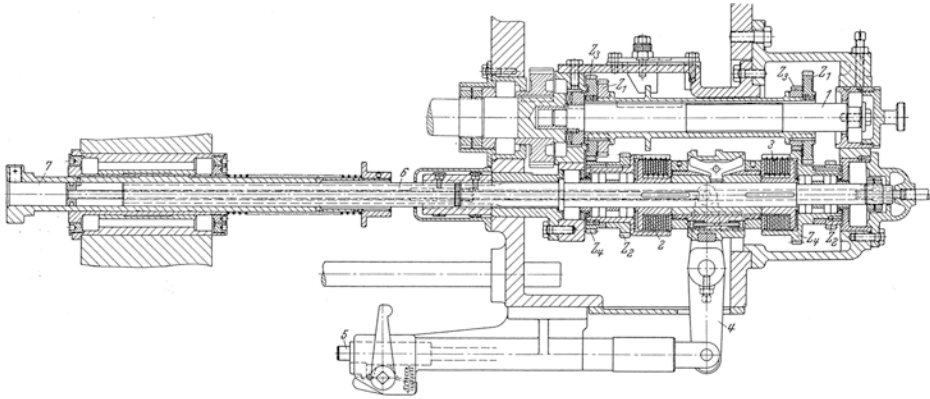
Gewindeschneideinrichtung mit Teleskopspindel und Getriebe im Antriebskasten [Fink38]
